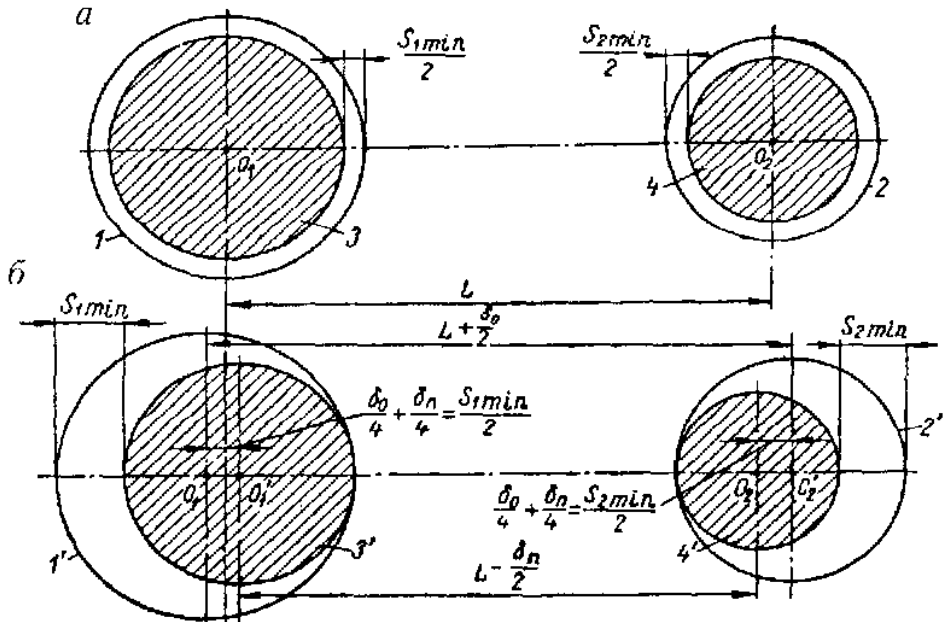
Розрахункові схеми для встановлення заготовки на два циліндричних пальця
